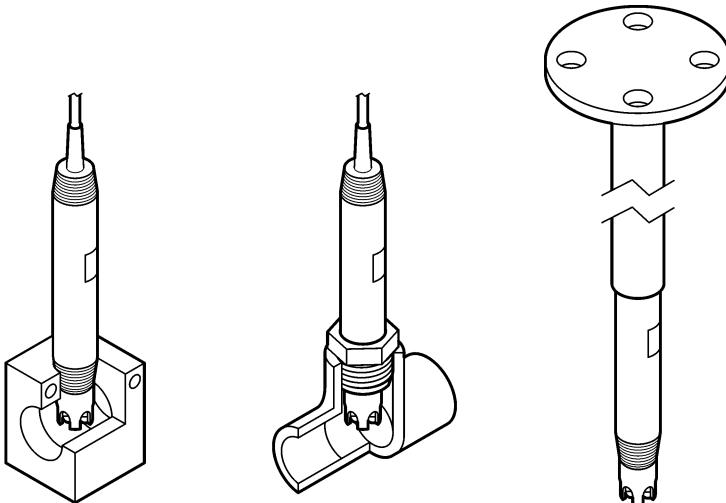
angiver sensorens dimensioner. Figur 5 viser monteringsmulighederne.
